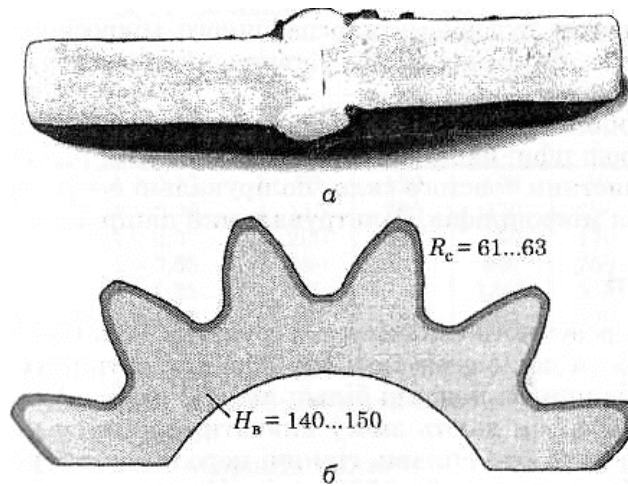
Макроструктура поверхні: а – зварного шва; б – шестерні
